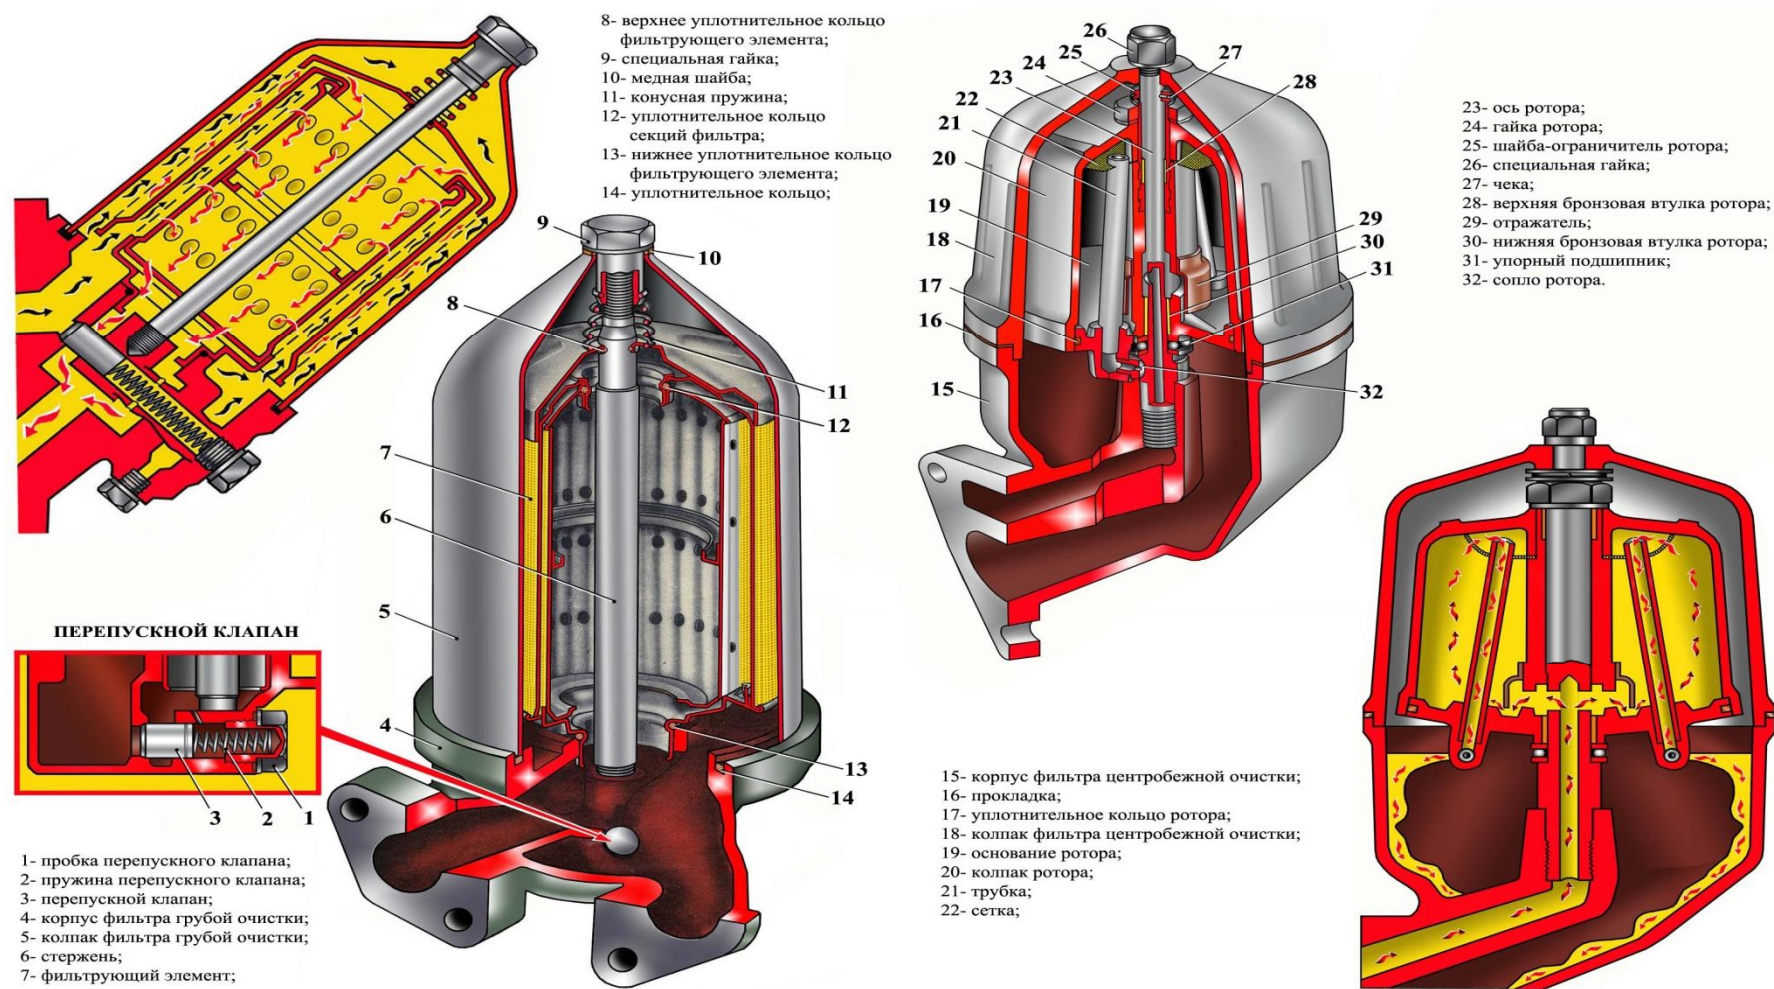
Фильтры системы смазки двигателя ЯМЗ-238
